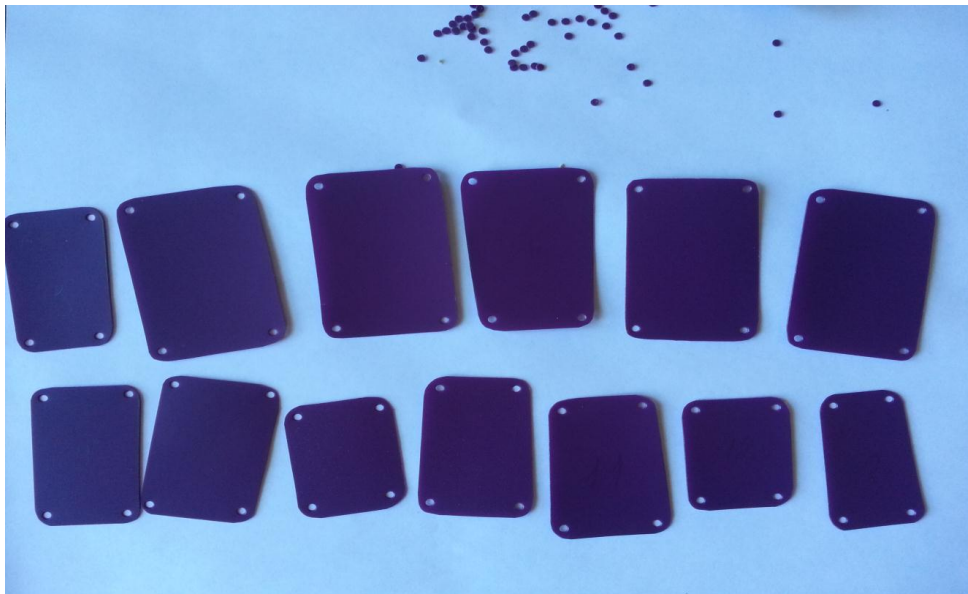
Внешний вид готовых деталей конструкции
